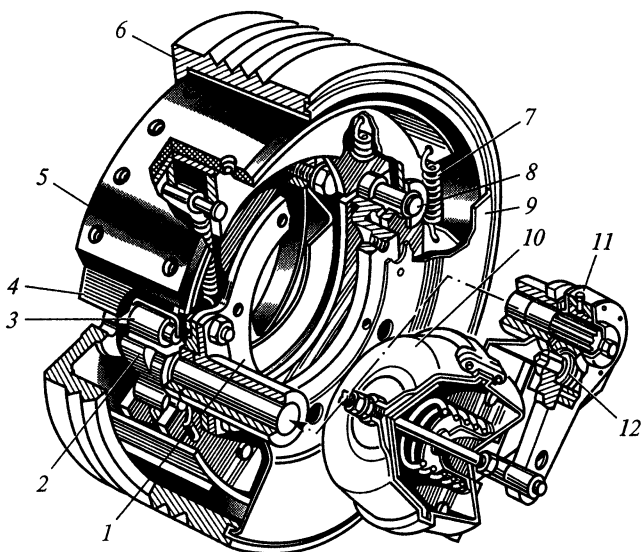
Колесный тормозной механизм грузовых автомобилей МАЗ:
